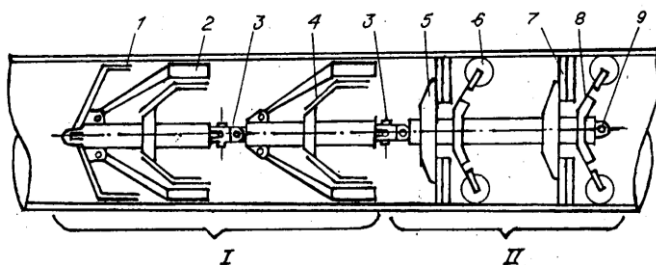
Устройство для гидромеханической очистки внутренней поверхности трубопровода: I – очистительный механизм; II – движительный механизм; 1 – центрирующие рессоры; 2 – нож; 3 – шарнирное соединение; 4 – прижимные рессоры; 5 – поршень; 6 – ролик; 7 – манжета; 8 – упругий элемент; 9 – место установки контролирующего прибора.
